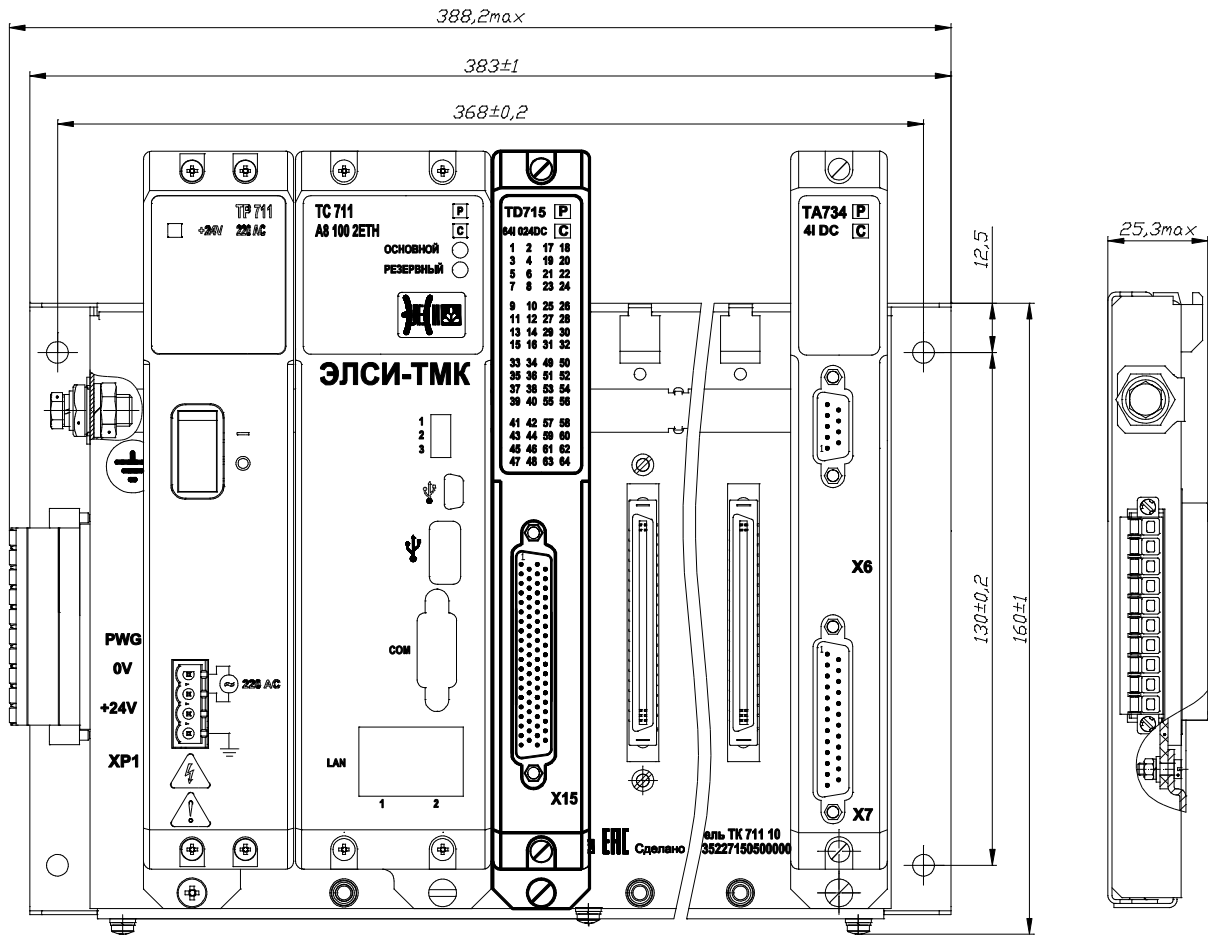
Внешний вид и габаритно-установочные размеры контроллера
